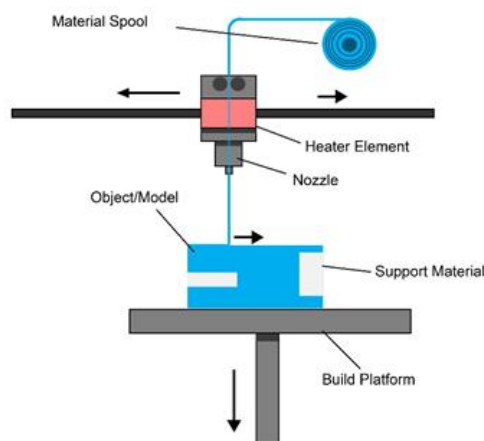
Esquema de la tecnología de extrusión de material. Fuente: [14].
